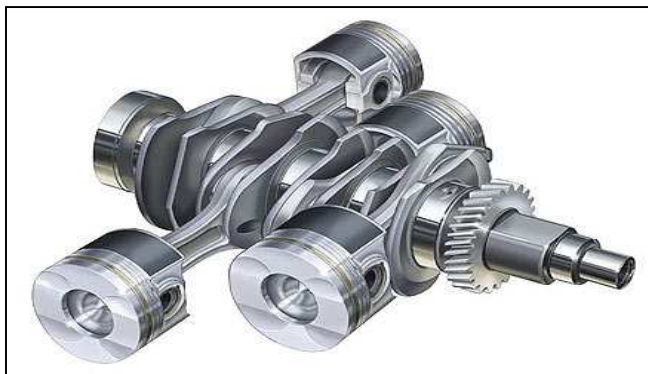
MOTOR BOXER – 4 CILINDROS
